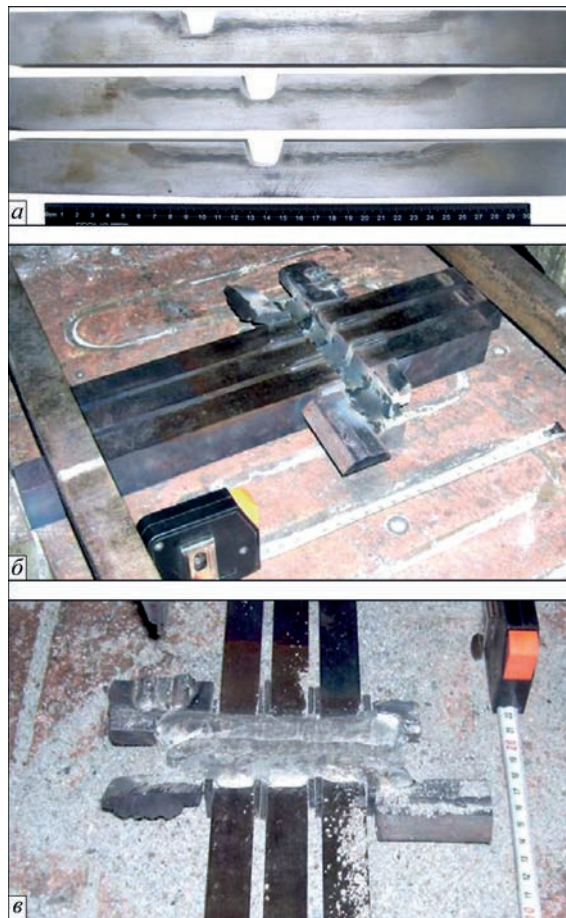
Зовнішній вигляд заготовок з розробленням під ремонтне наплавлення (а), зібраних у пакет до (б) та після ремонтного наплавлення (в)
